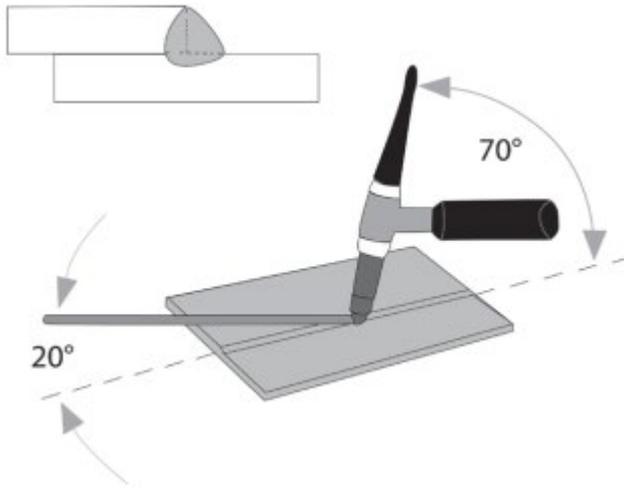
Положення «TIG-пальника» під час виконання зварювання з'єднання в напуск.
